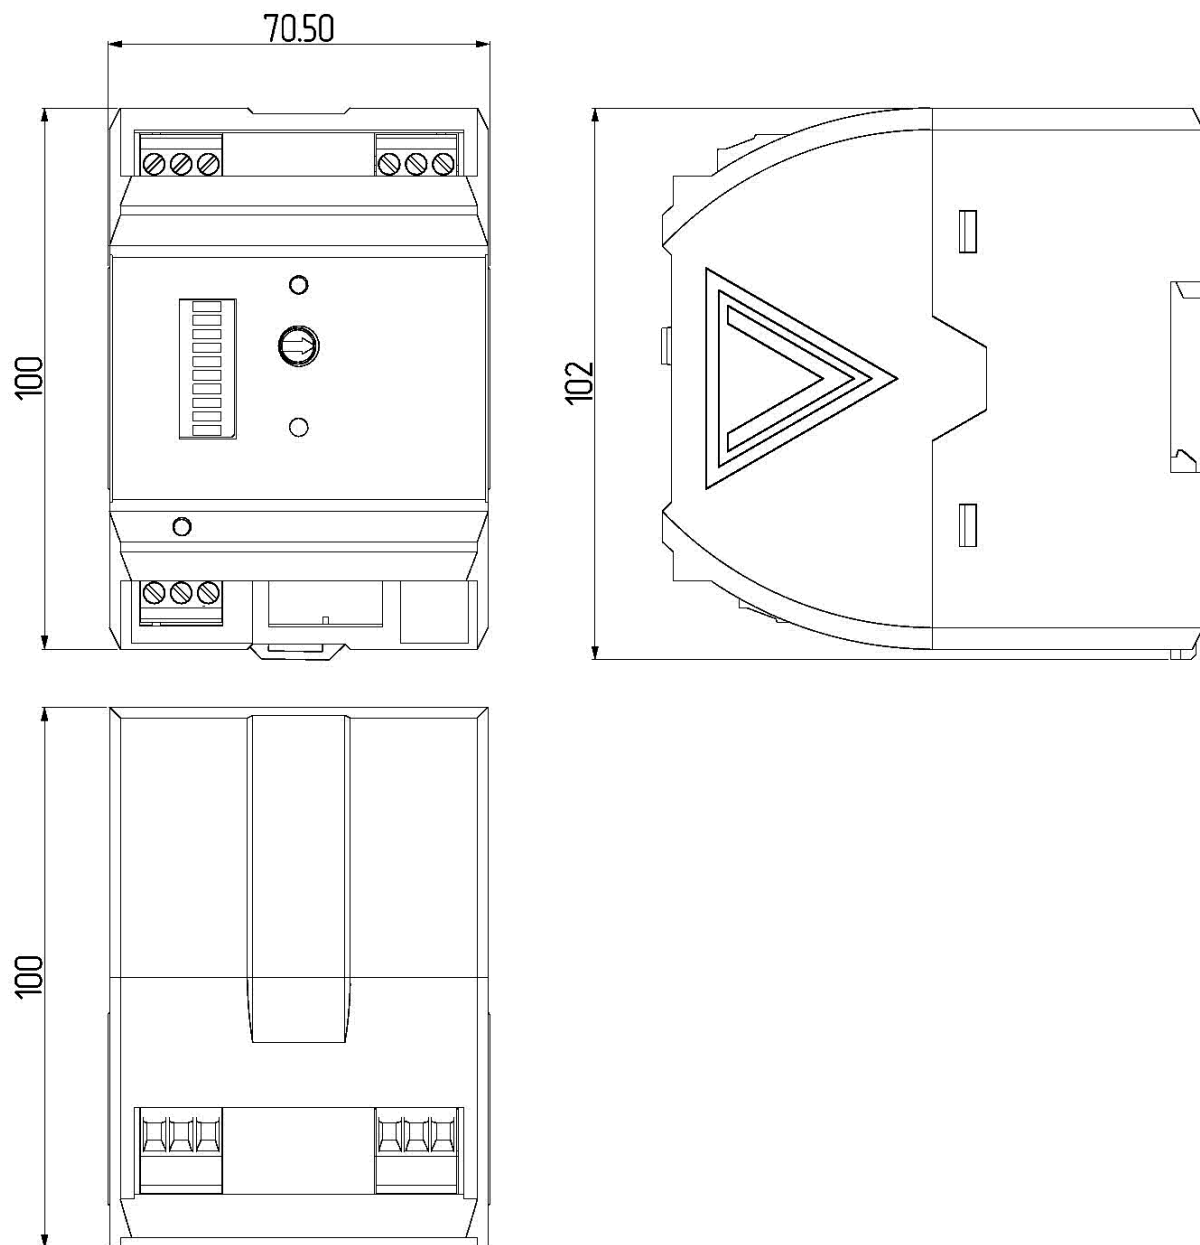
Внешний вид. Габаритный чертёж РКСИ-1002
